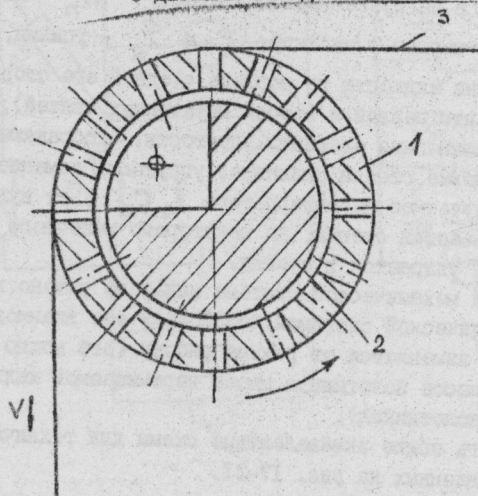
Схема конструкции верньерно-шкального устройства с двойным замедлением
